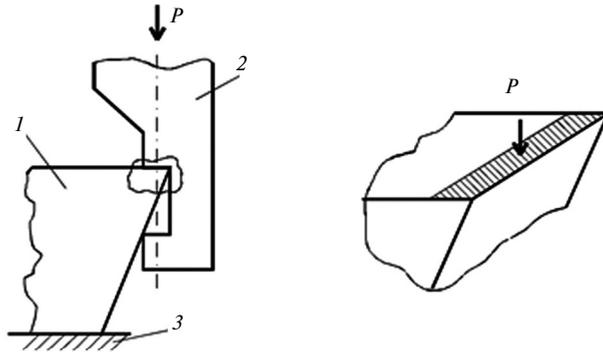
Схема консольного изгиба неперетачиваемых режущих пластин: 1 – нагружающий элемент; 2 – режущая пластина; 3 – опора.
